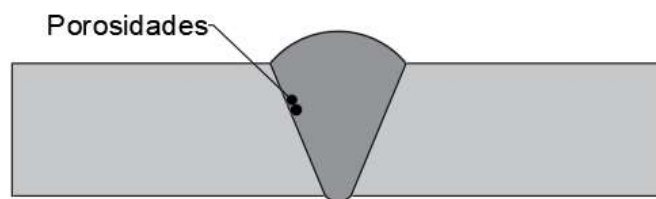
Ilustração esquemática de porosidades presentes num cordão de soldadura.
